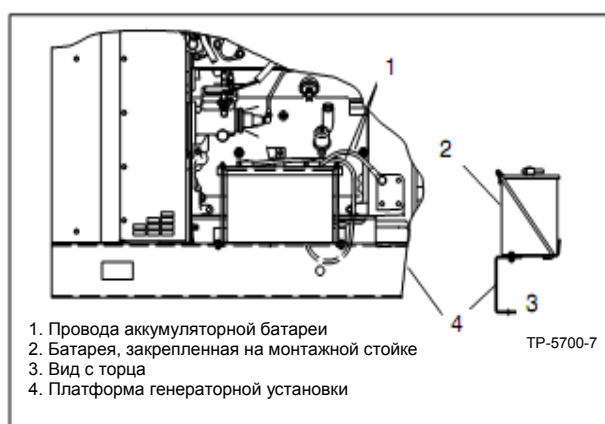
Стандартное размещение батареи, вид сбоку
